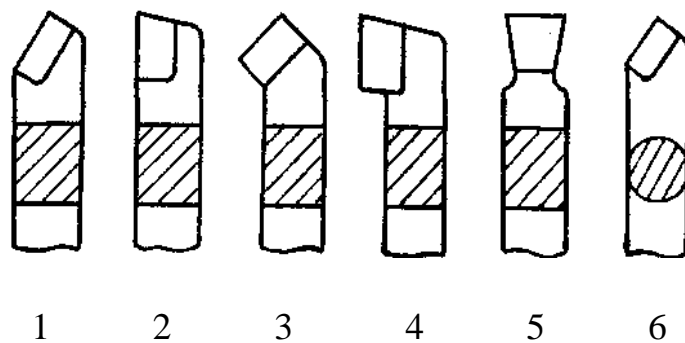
Резцы токарные: 1-; 2 -; 6-
